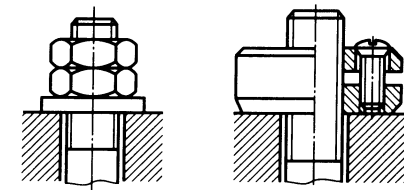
Способы стопорения дополнительной резьбовой деталью
